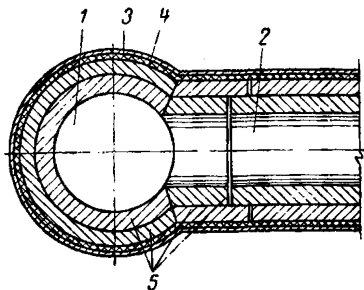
Стык цилиндрической футеровки с цилиндрическим патрубком
